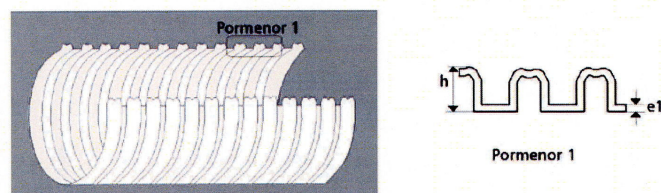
Perfil do tubo corrugado 2DREN de parede simples – tipo C1
